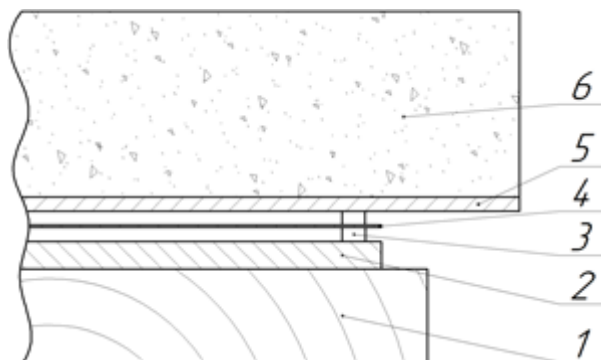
Схема сборки пластин под сварку взрывом:
